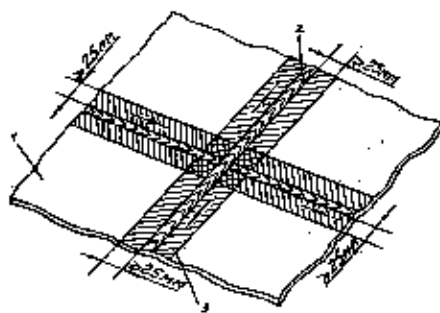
Схема упрочнения крестообразных сварных соединений:
